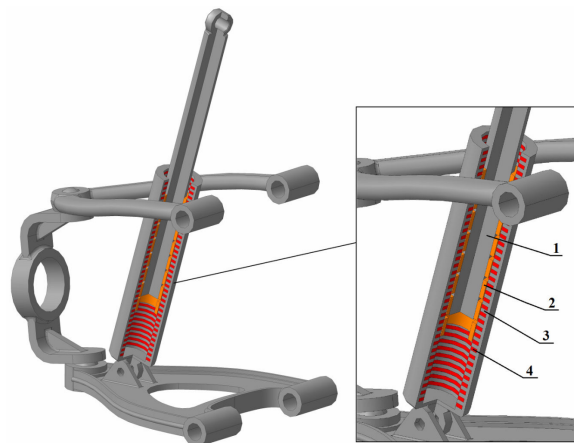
3D-модель основных элементов рычажной подвески автомобиля с ЭМП-амортизатором: 1 – ротор; 2 – постоянные магниты; 3 – корпус; 4 – катушки обмоток фаз
